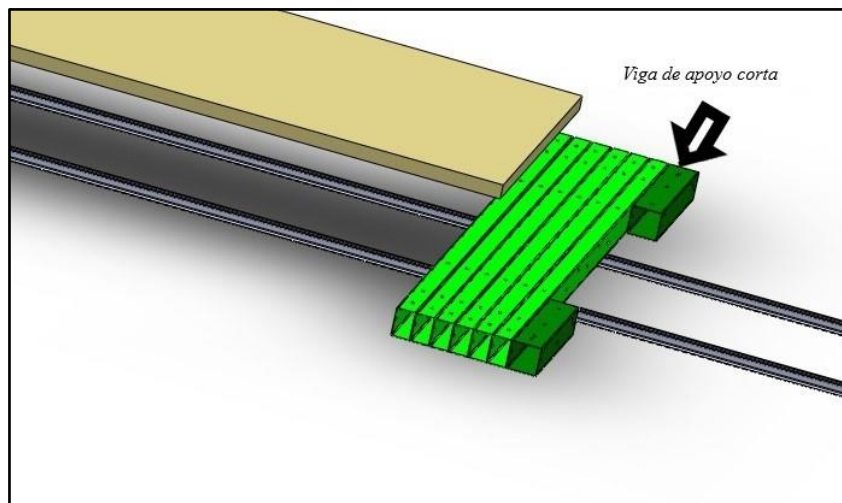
Viga de apoyo corta. Fuente: Diseño propio.
